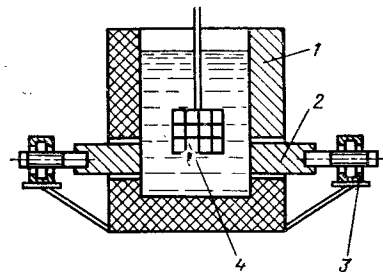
Однофазная печь-ванна для нагрева заготовок в соляном растворе
